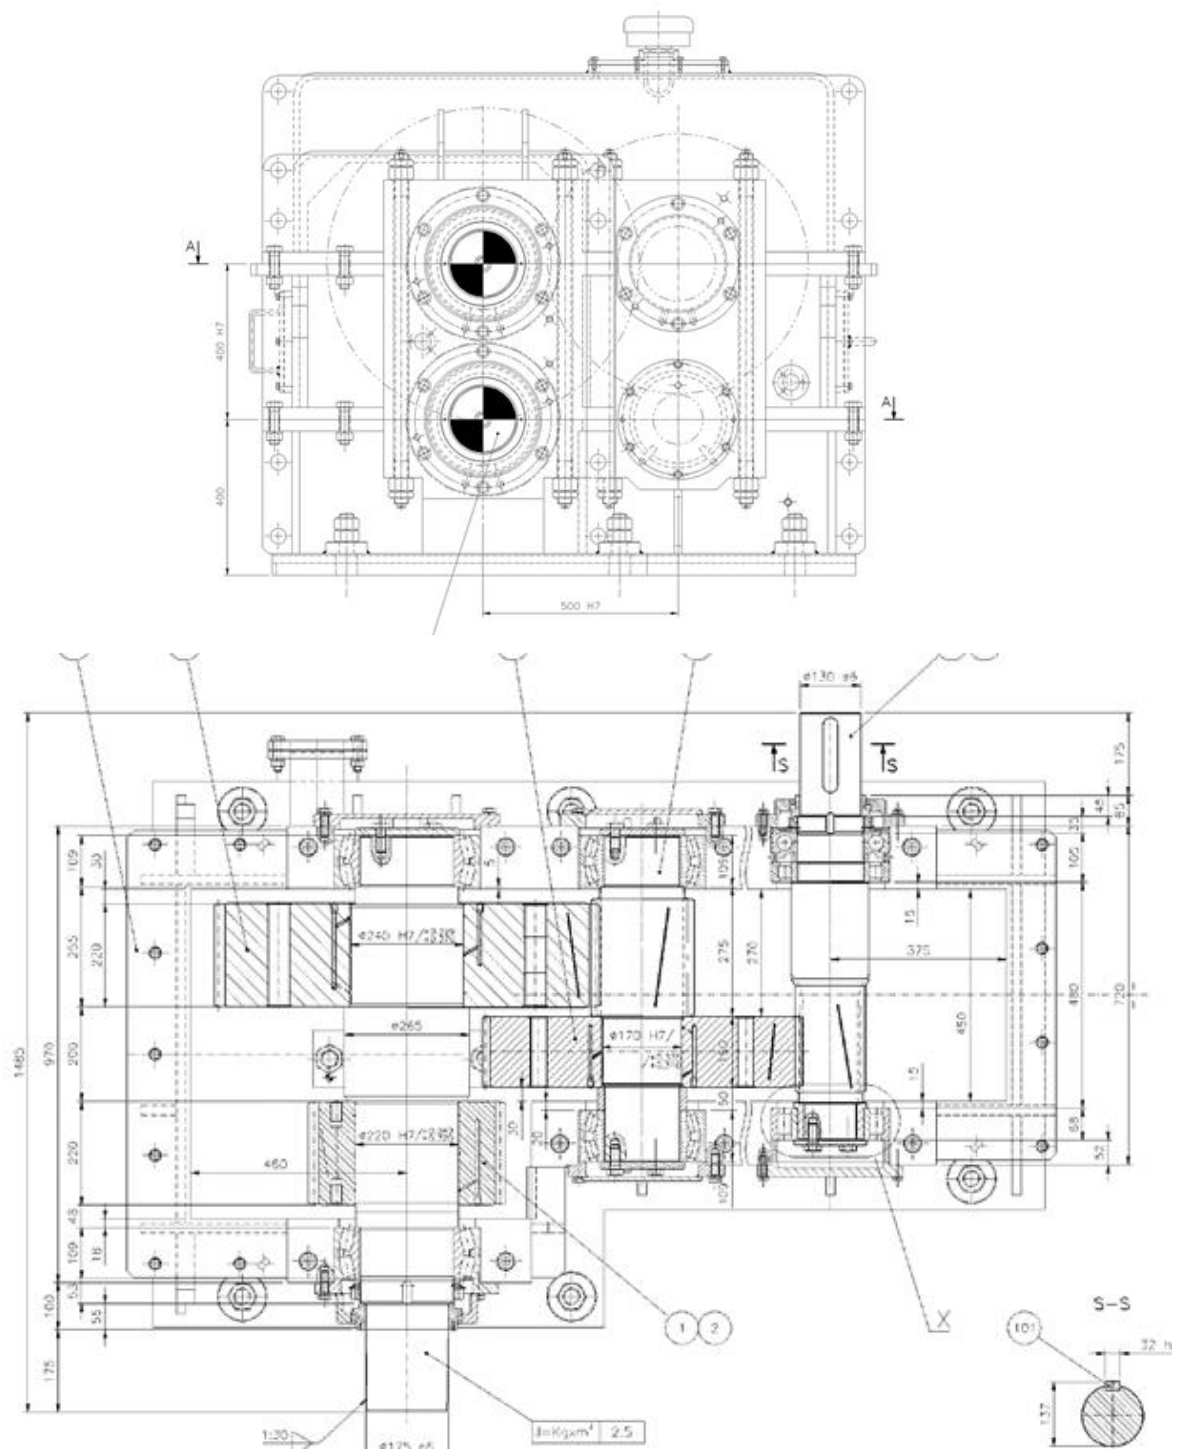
Загальний вид комбінованого редуктору та його кінематична схема
